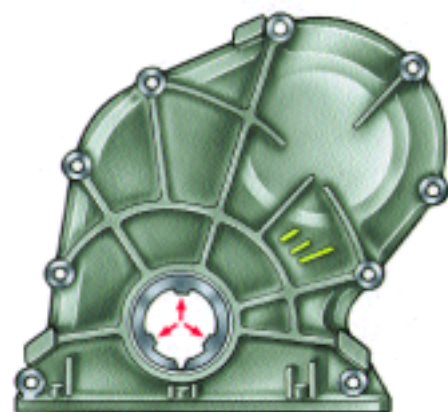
Крышка привода распределительного вала двигателя мод. 2106-70 (стрелками показаны выступы для центрирования крышки относительно ступицы шкива коленчатого вала)
